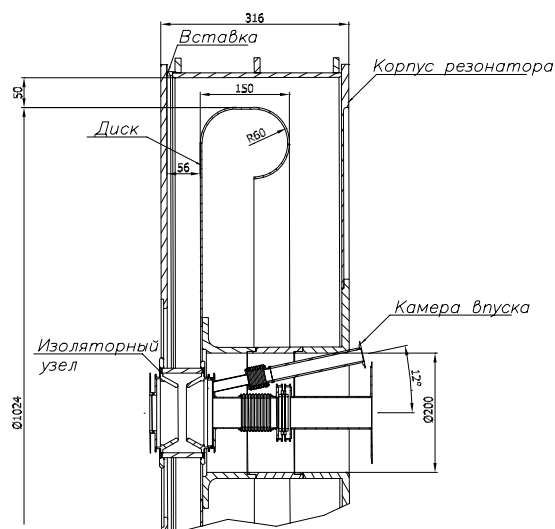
Чертеж резонатора накопителя «Сибирь-1»
